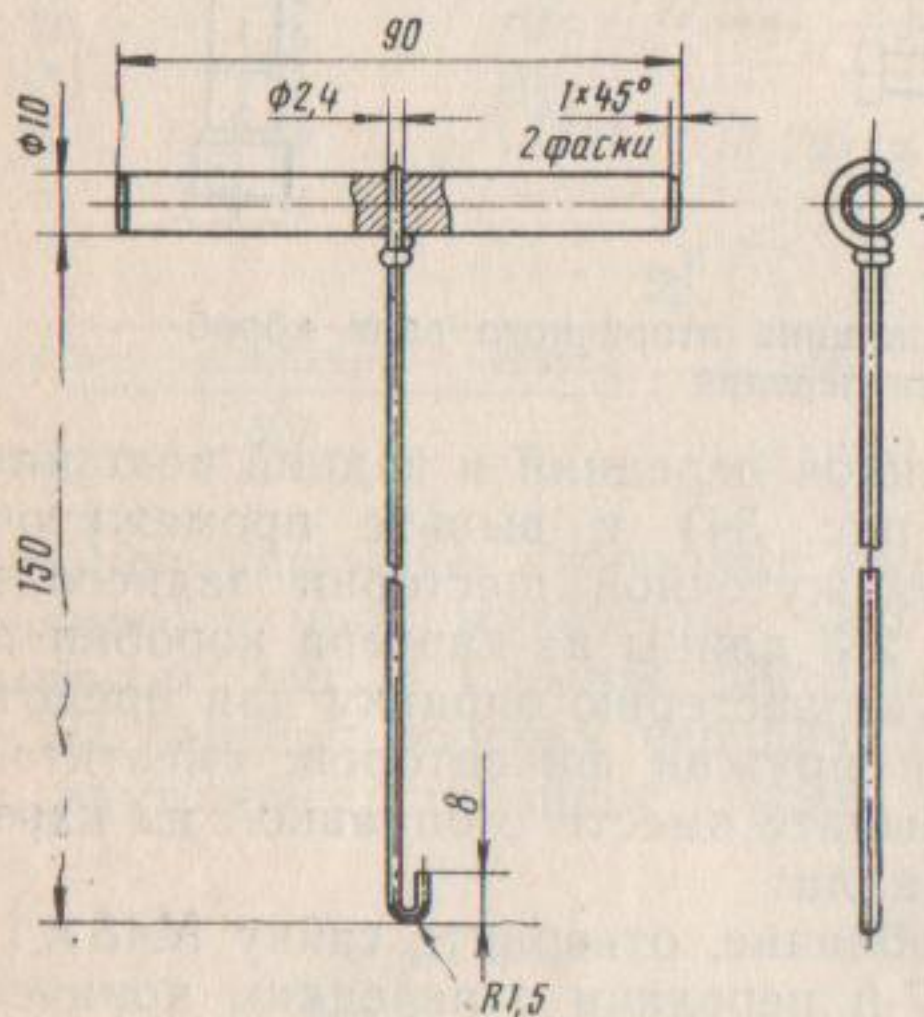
Крючок для демонтажа пружин синхронизатора коробки передач
